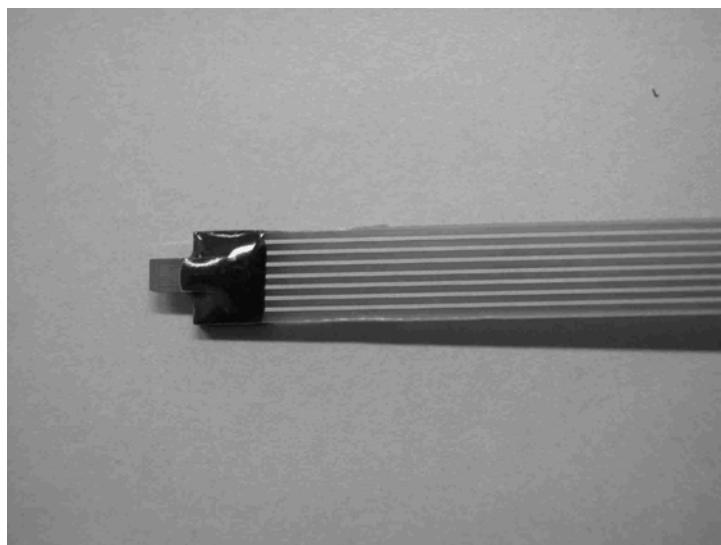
Enrobage époxy sur PCB recouvert d'un vernis épargne.
